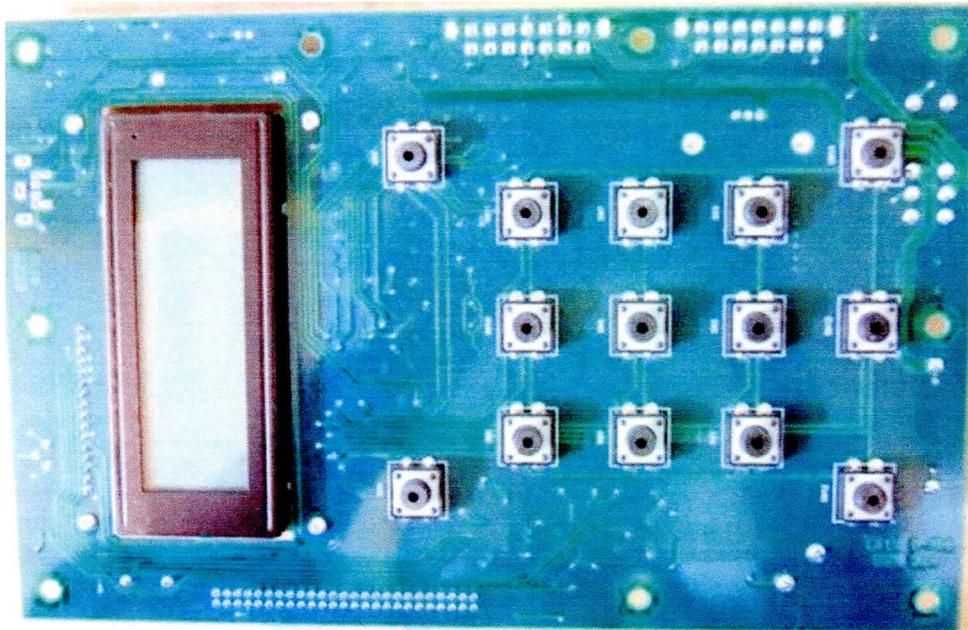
Tarjeta LOCAL PRESET identificada con número de parte 110792 revisión B vista cara de soldadura.
